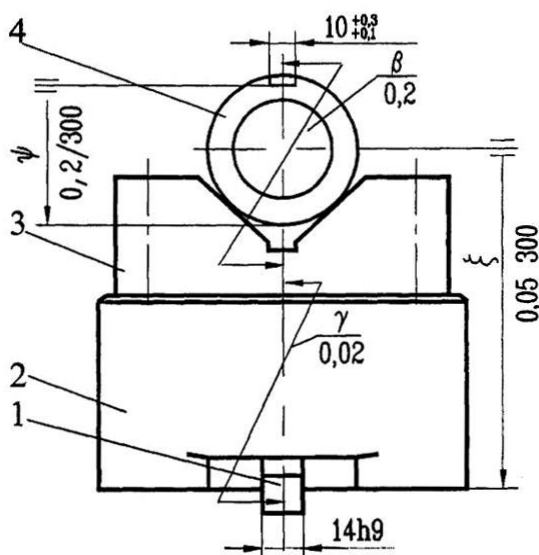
Принципиальная конструктивная схема приспособления для фрезерования паза:
